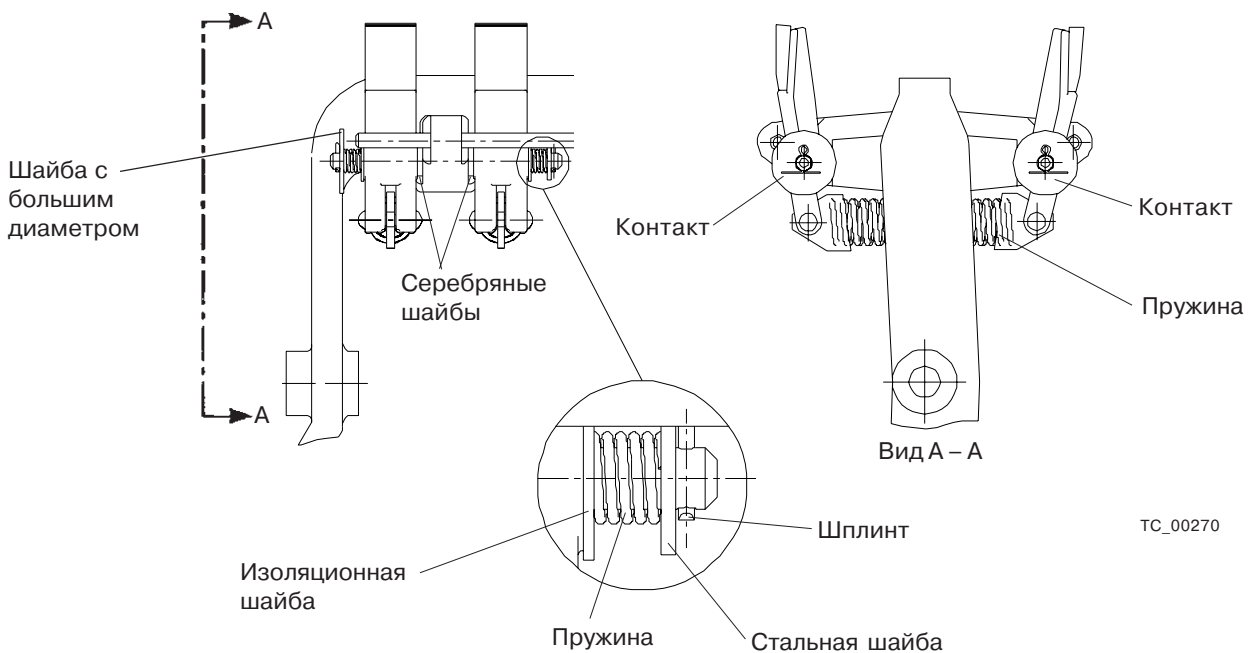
Подвижные основные контакты с наконечниками из меди-вольфрама, шайбами и пружинами
